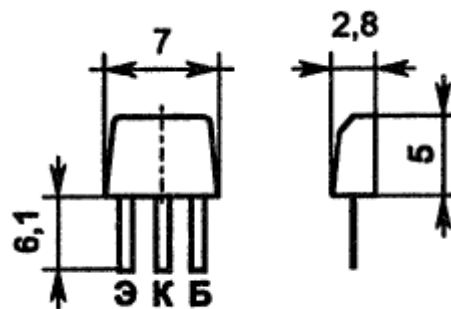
Габаритні розміри транзистора типу КТ315Б
